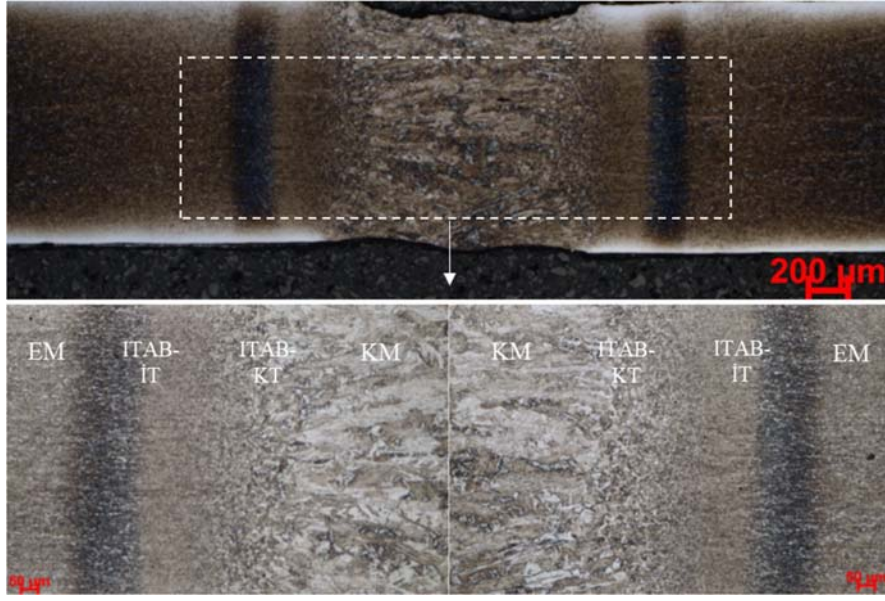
Lazer Kaynak Deney 1- Kaynak metal mikroyapı görüntüsü (Laser Welding Trial 1 – Microstructure of weld metal)
